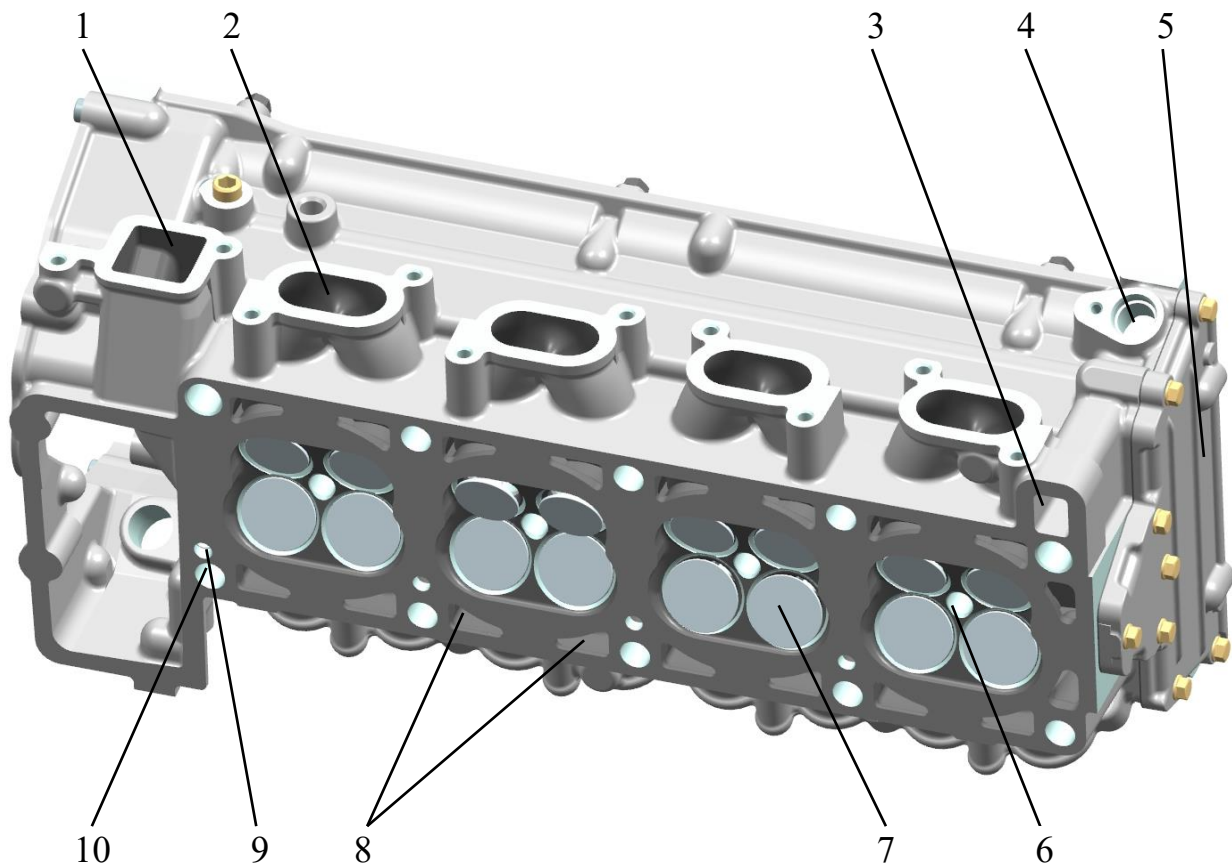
Головка цилиндров. Вид на камеры сгорания, фланец выпускного коллектора и заднюю крышку:
